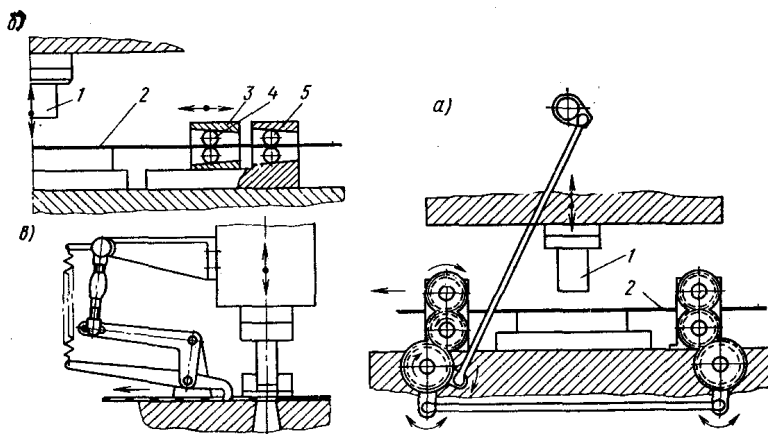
Схемы устройств для шаговой подачи непрерывных заготовок:
